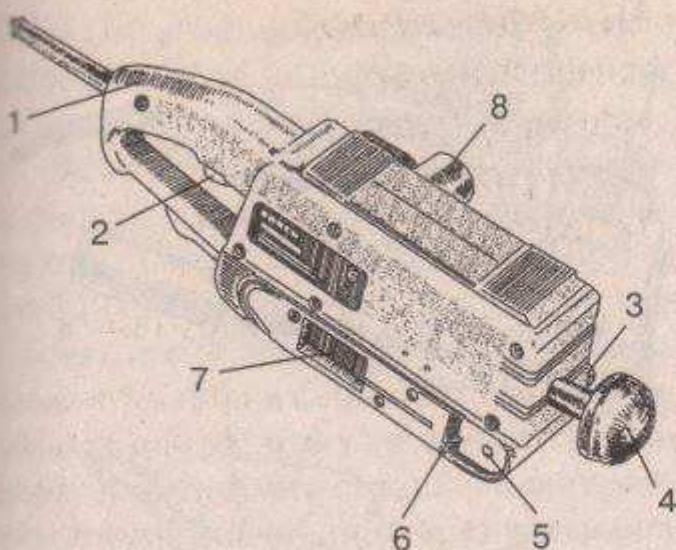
Ручная ленточная шлифовальная машина: 1 — ручка; 2 — кнопка-курок; 3 — кнопка регулирования расположения ленты; 4 — вспомогательная ручка; 5 — вал; 6 — лента; 7 — рычаг освобождения натяжения ремня; 8 — патрубок пылеудаления
